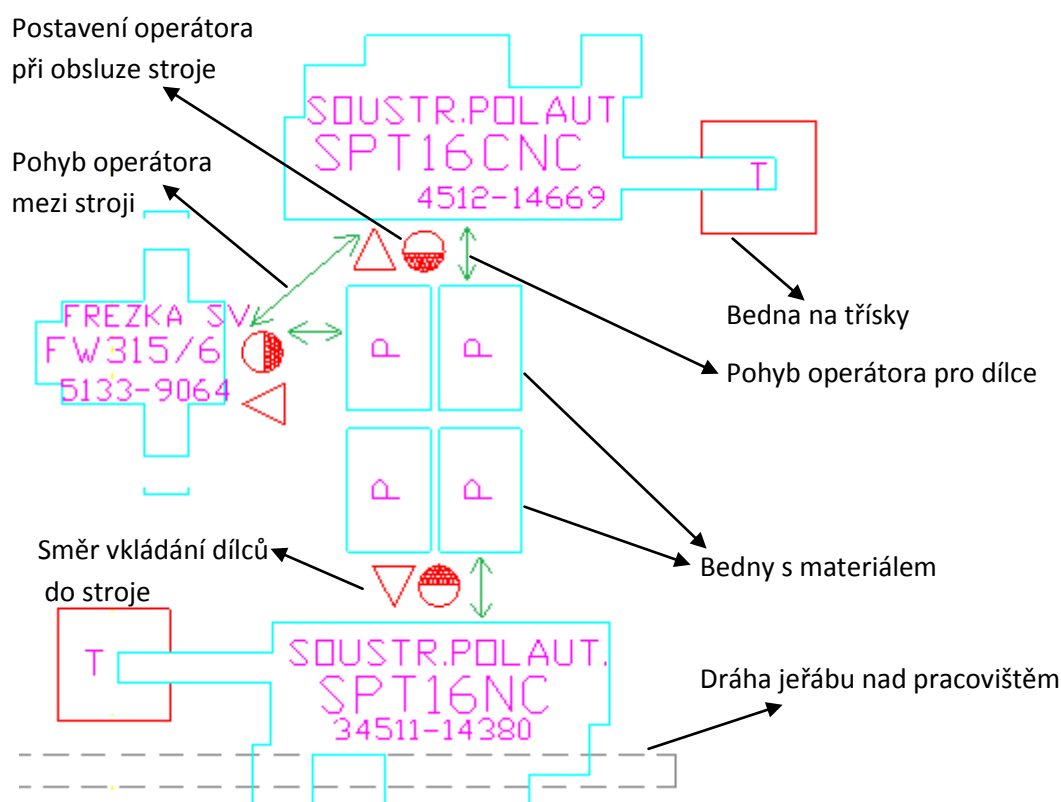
Poloautomatický soustruh SPT 16 CNC
